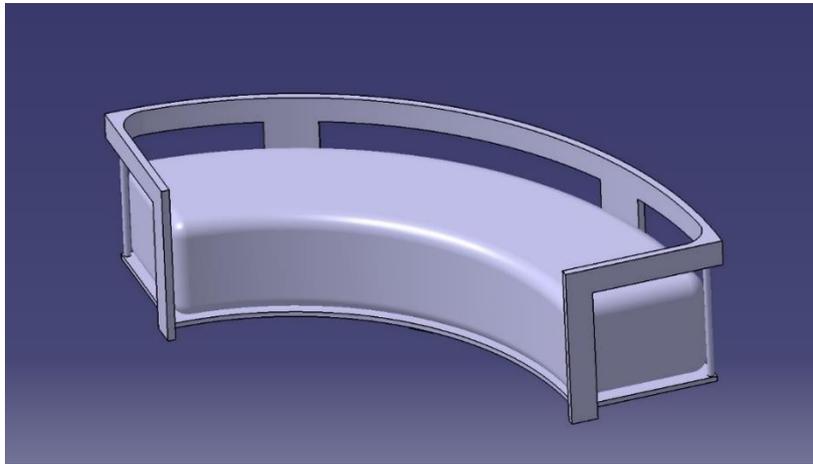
Conjunto semicúpula, apoyo y estanterías
